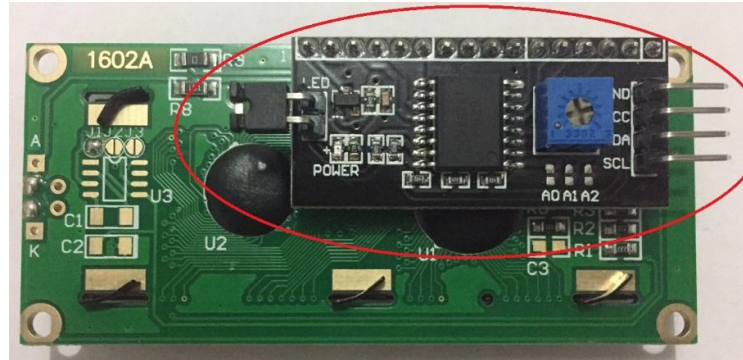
Módulo I2C soldado ao display LCD.
